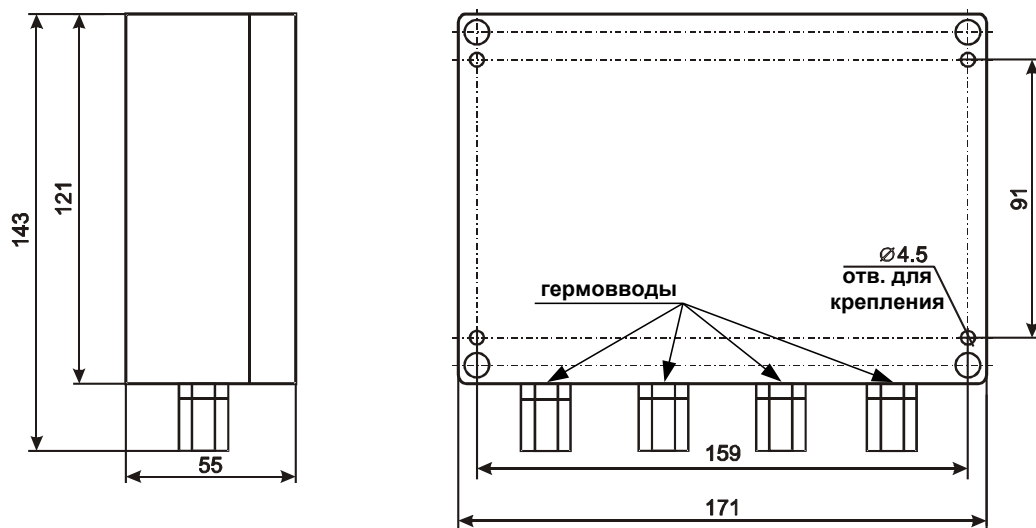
Внешний вид и габаритные размеры БЦП в корпусе IP65
